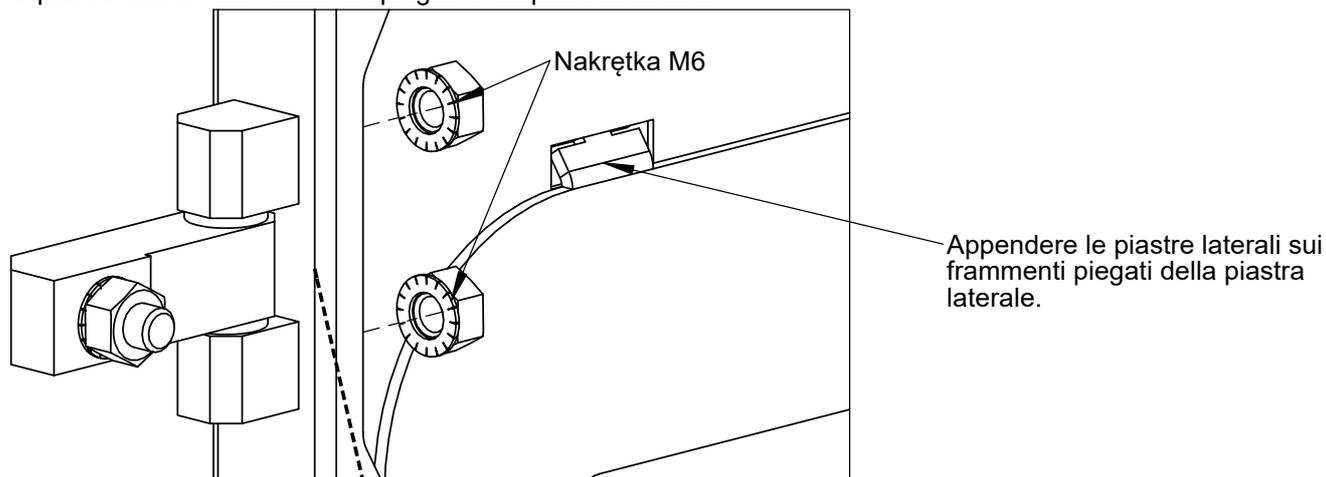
Installazione delle cerniere sulle piastre laterali AC520-452 (dadi M6).
